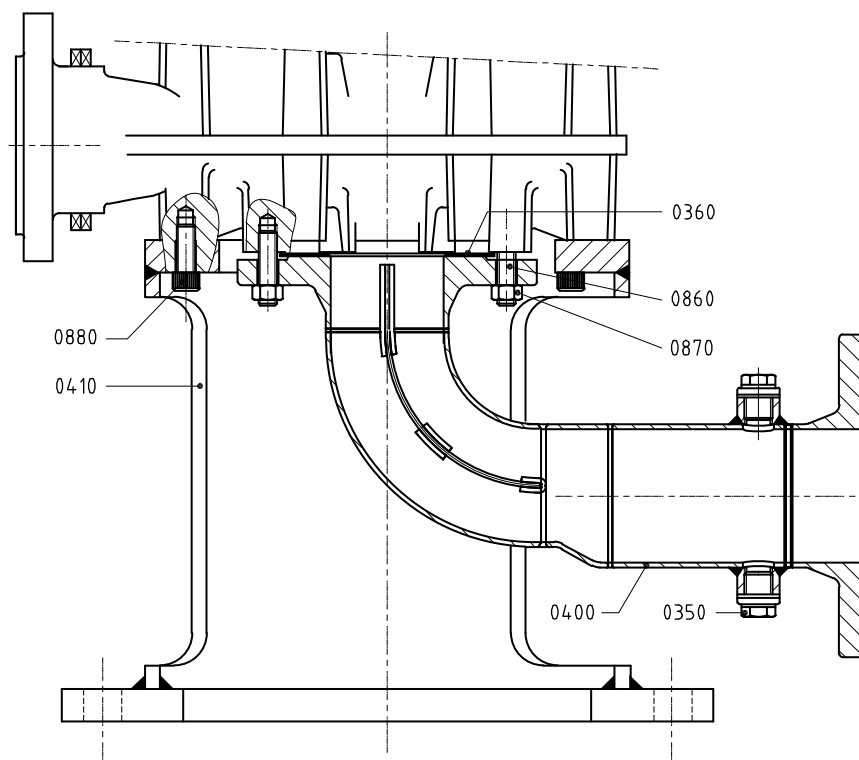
Чертеж в разрезе приемный патрубок 200–200 / 250В–315.
